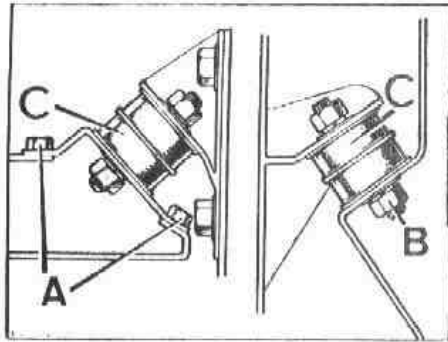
Desmontaje de los tacos de apoyo del motor
